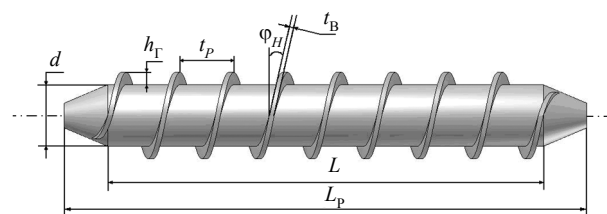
Роторно-винтовой двигатель:  $d$  – диаметр базового цилиндра ротора;  $L$  – длина базового цилиндра ротора;  $L_p$  – общая длина ротора;  $h_{\Gamma}$  – высота винтовой лопасти шнека;  $\varphi_H$  – угол подъема винтовой лопасти у ее основания;  $t_P$  – шаг винтовой лопасти;  $t_B$  – толщина винтовой лопасти
